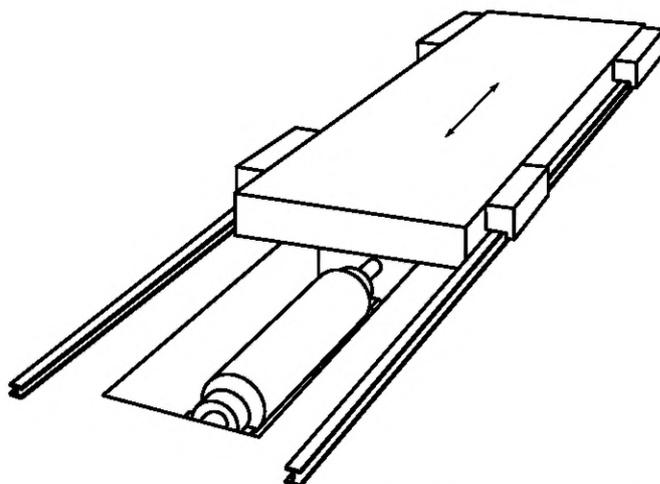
Прямо́к с кры́шкой для высо́коскоростного баланси́ровочного станка
